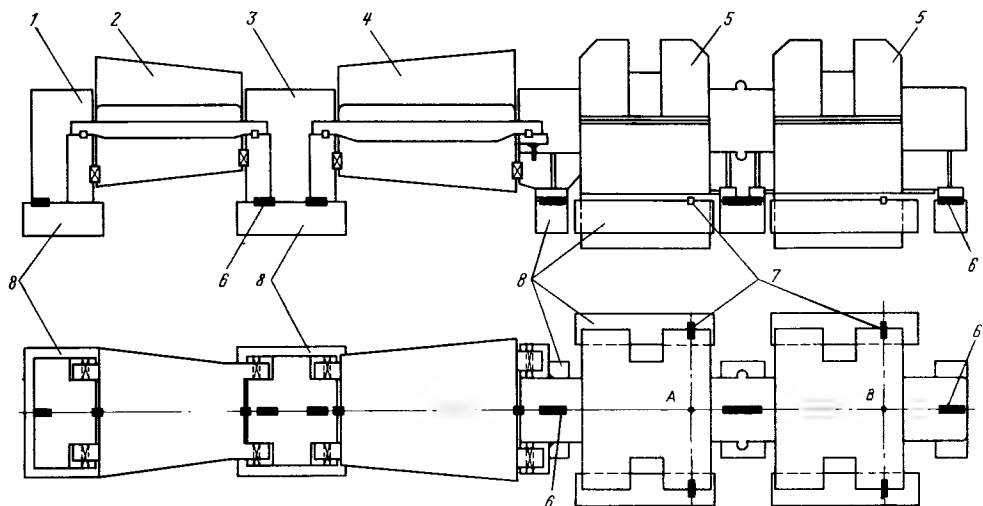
Установка многоцилиндровой турбины на фундаменте:
